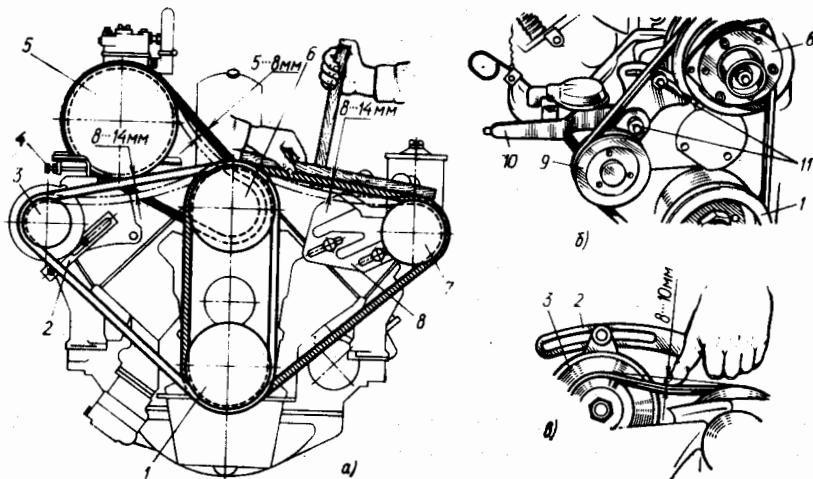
Контроль и регулировка натяжения приводных ремней двигателей автомобилей:
